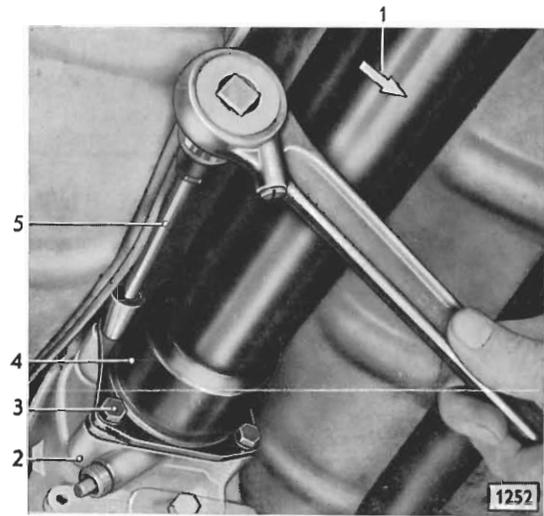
Stützrohr an der oberen Befestigung vom Getriebe abschrauben
